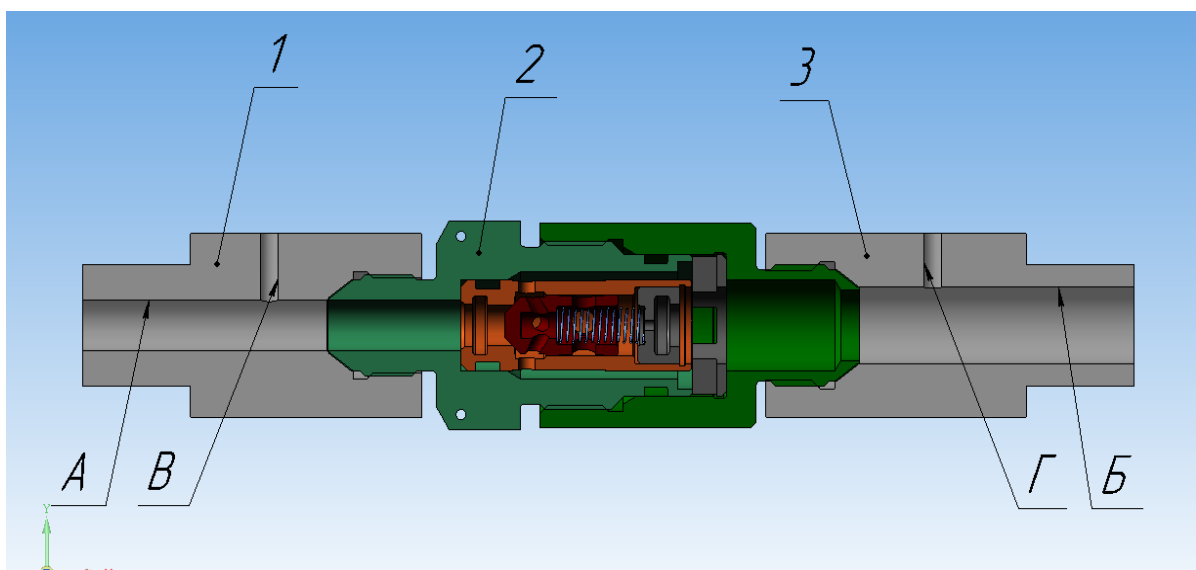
3D-модель сборки для снятия статической характеристики ОК
